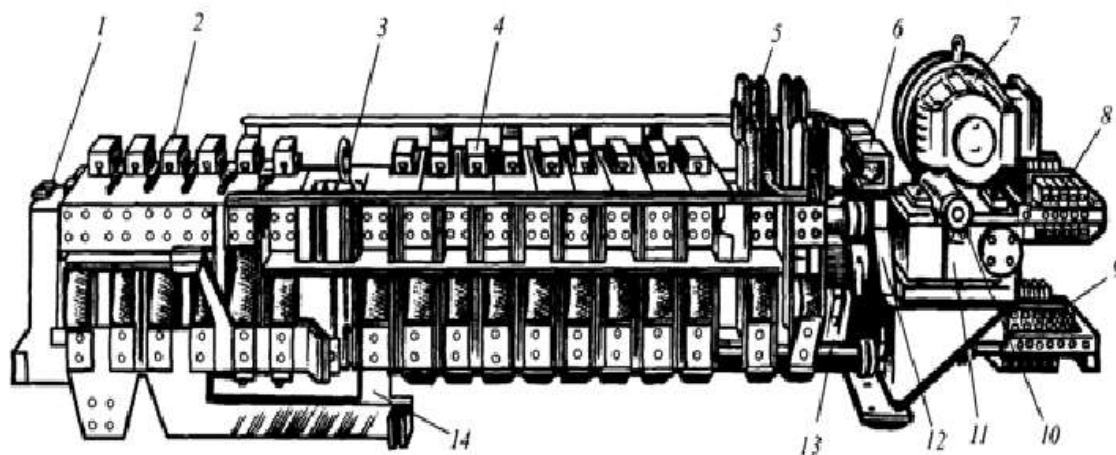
Общий вид главного контроллера ЭКГ-8Ж
